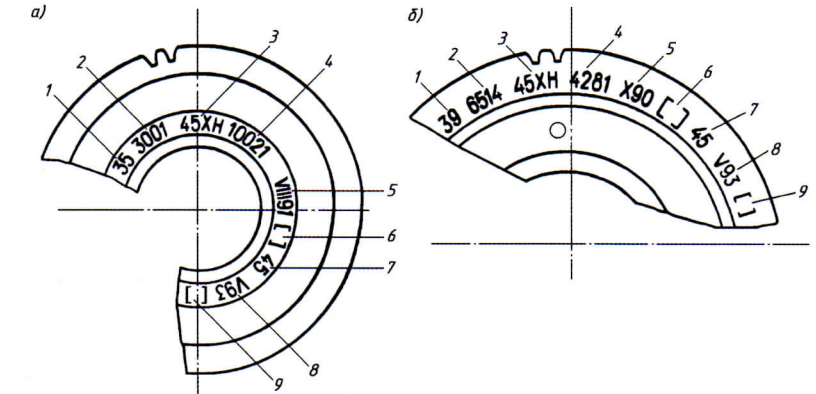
Знаки и клейма на зубчатом колесе (а) и на венце зубчатого колеса (б):
